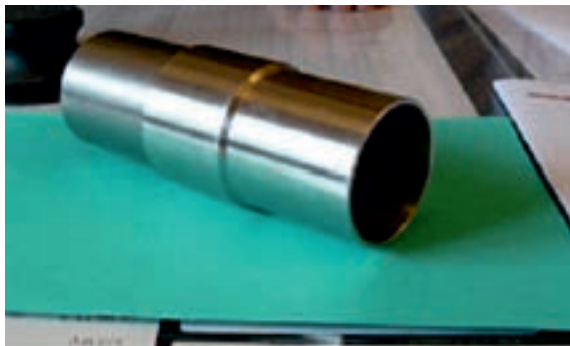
Пилотный образец биметаллической трубки, изготовленный из китайского титана и австрийской стали
